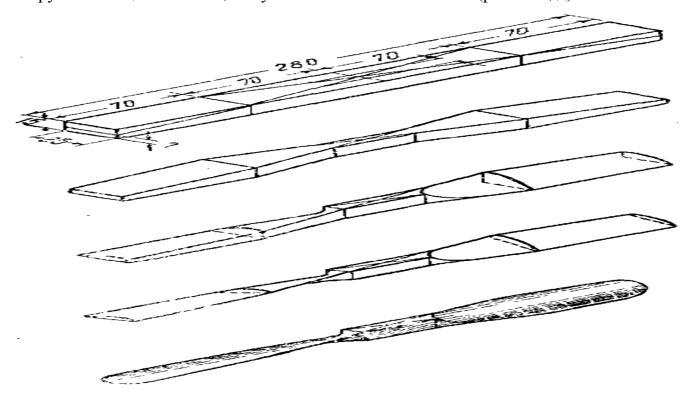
, Процесс изготовления винта: а — расчерчивание бруска: б — заготовка; в — обработка передних сторси лопастей; г — обработка задних лопастей; д — окончательная форма винта
